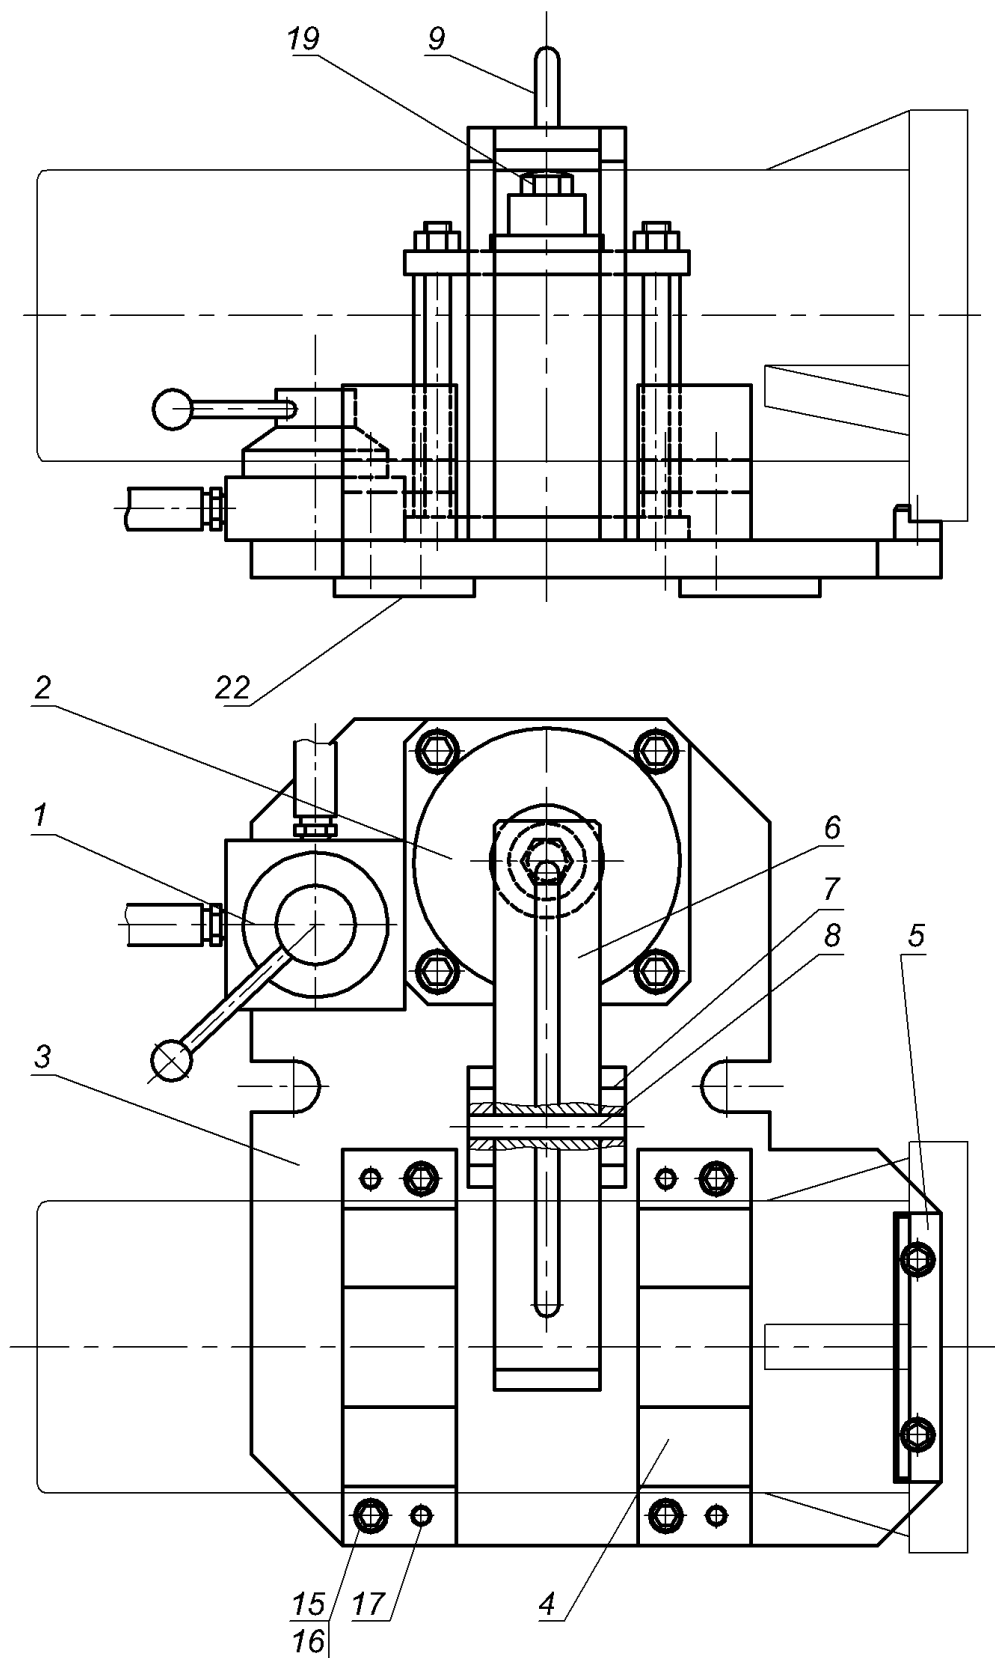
Загальний вигляд фрезерного пристрою:
